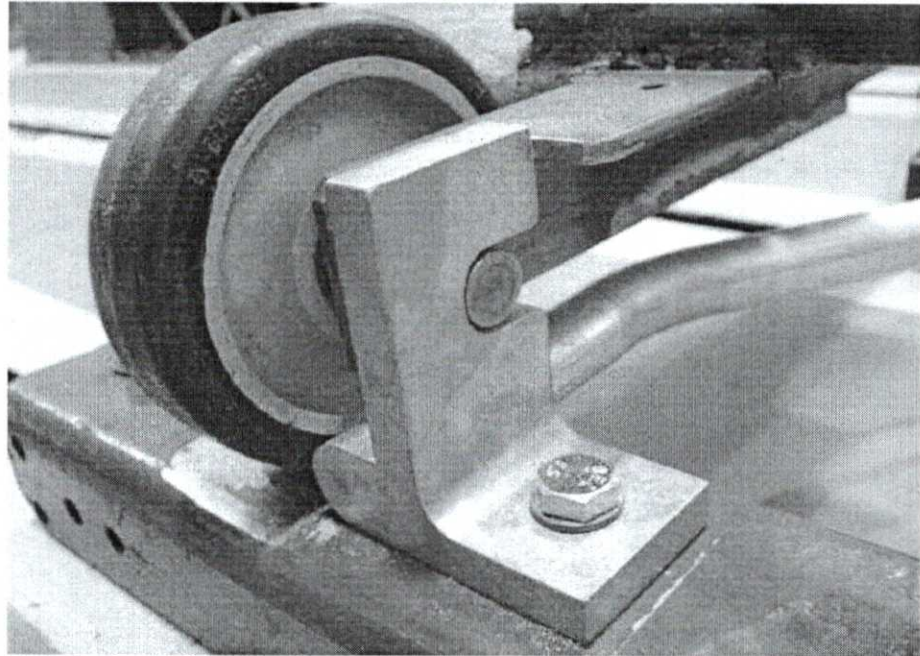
Lado esquerdo da amostra 2 após ensaio.
